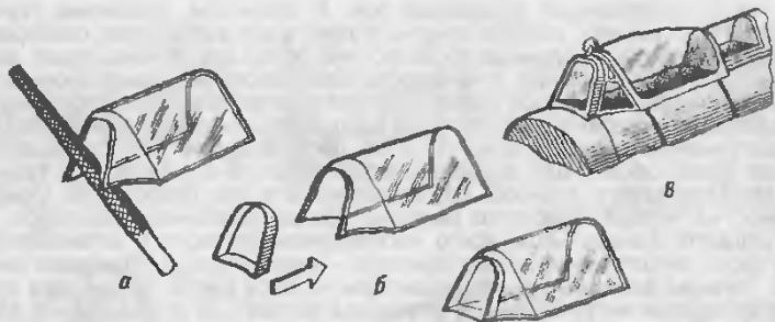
Нестандартные фонари: а - выборка лобового участка фонаря под бронестекло; б - вклейка бронестекла с размещением его внутри; в - образец фонаря с выступающим наружу бронестеклом ("Слитфайр")
